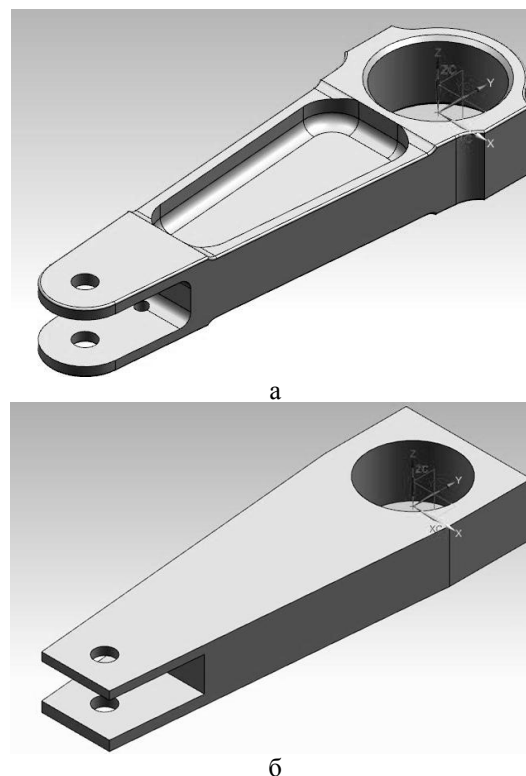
Геометрия детали, выполненной согласно КД (а) и «заготовки», подлежащей оптимизации (б)
